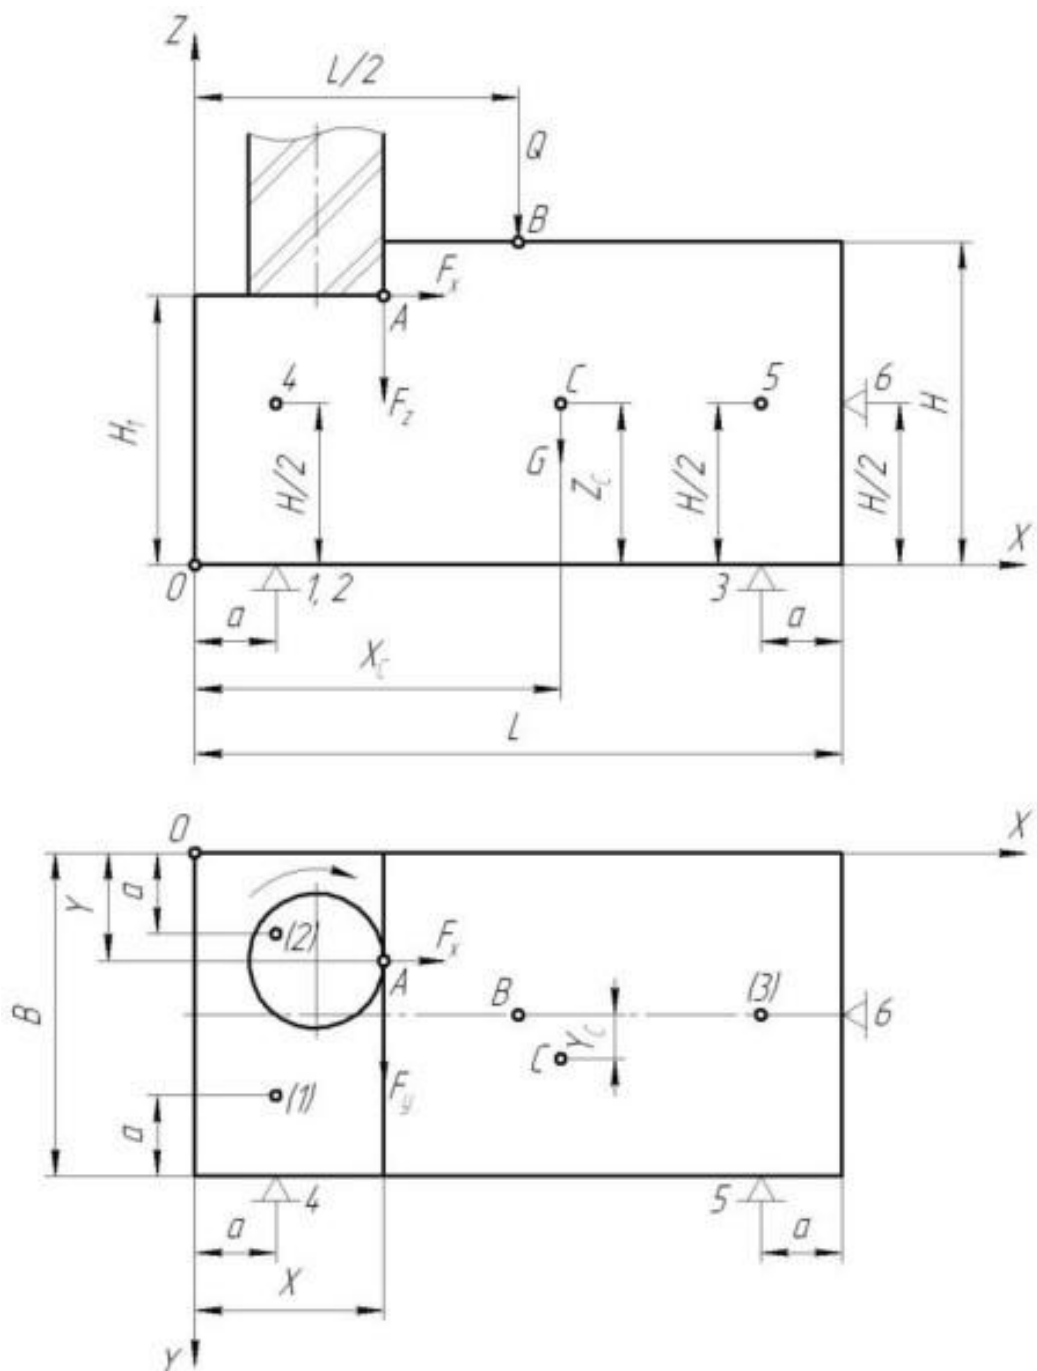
Розрахункова схема механічної системи «пристрій–заготовка»
